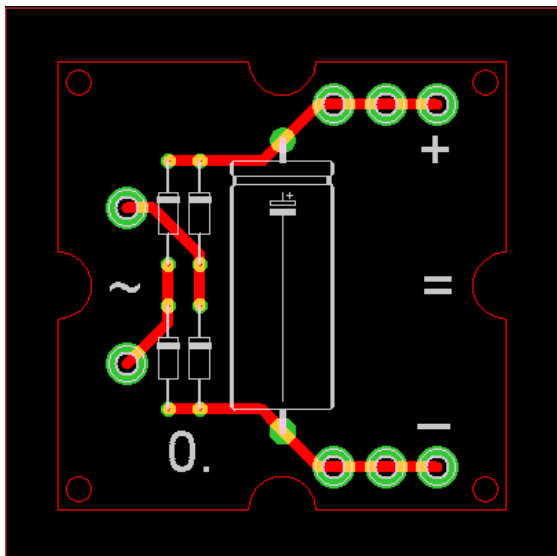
Nachbau 3: Platinenentwurf für 60er Kassetten ([32076](#))
